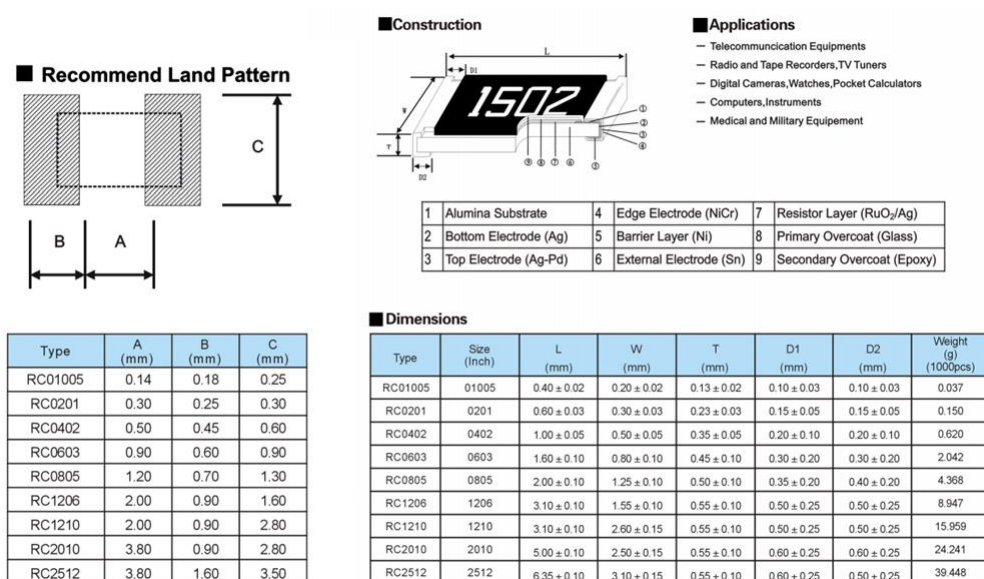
Цоколевка и размеры резисторов
